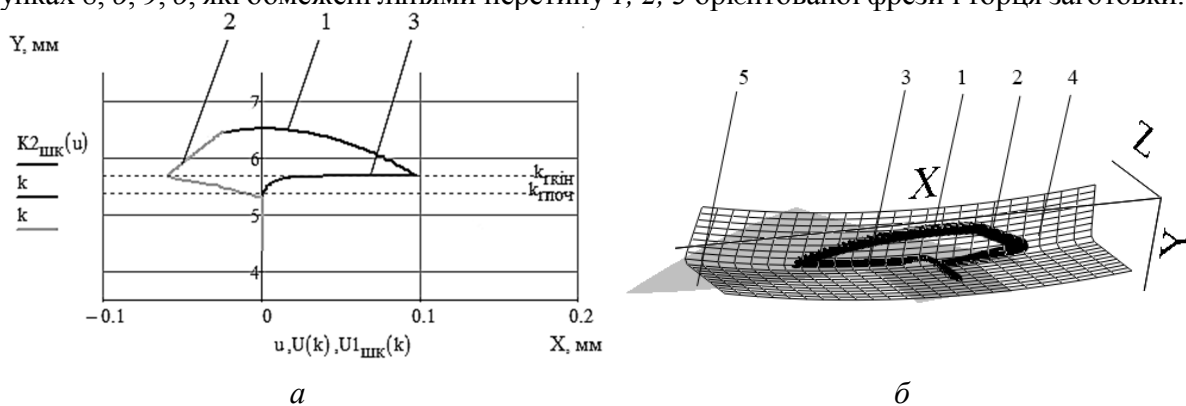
Пляма контакту фрези й кулачка розподільного вала при обробці ділянки кулачка, центр якої збігається з центром кулачка
